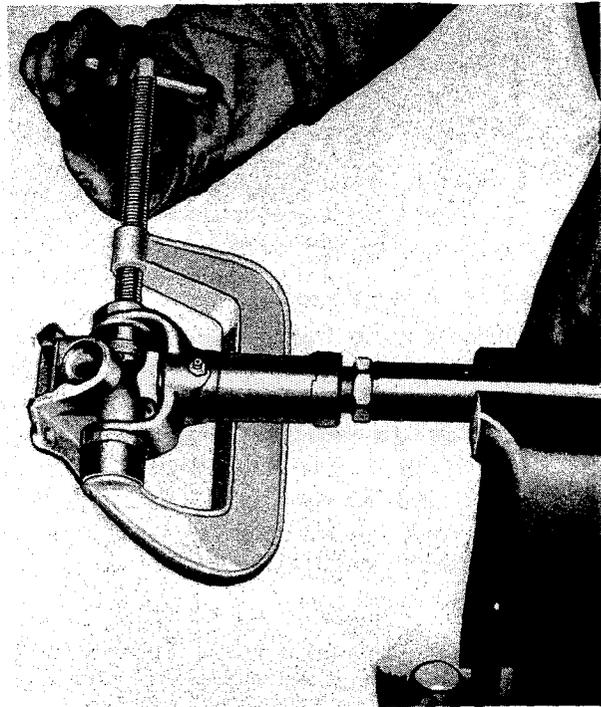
Werkzeug für Einbau der Lagerbüchsen
